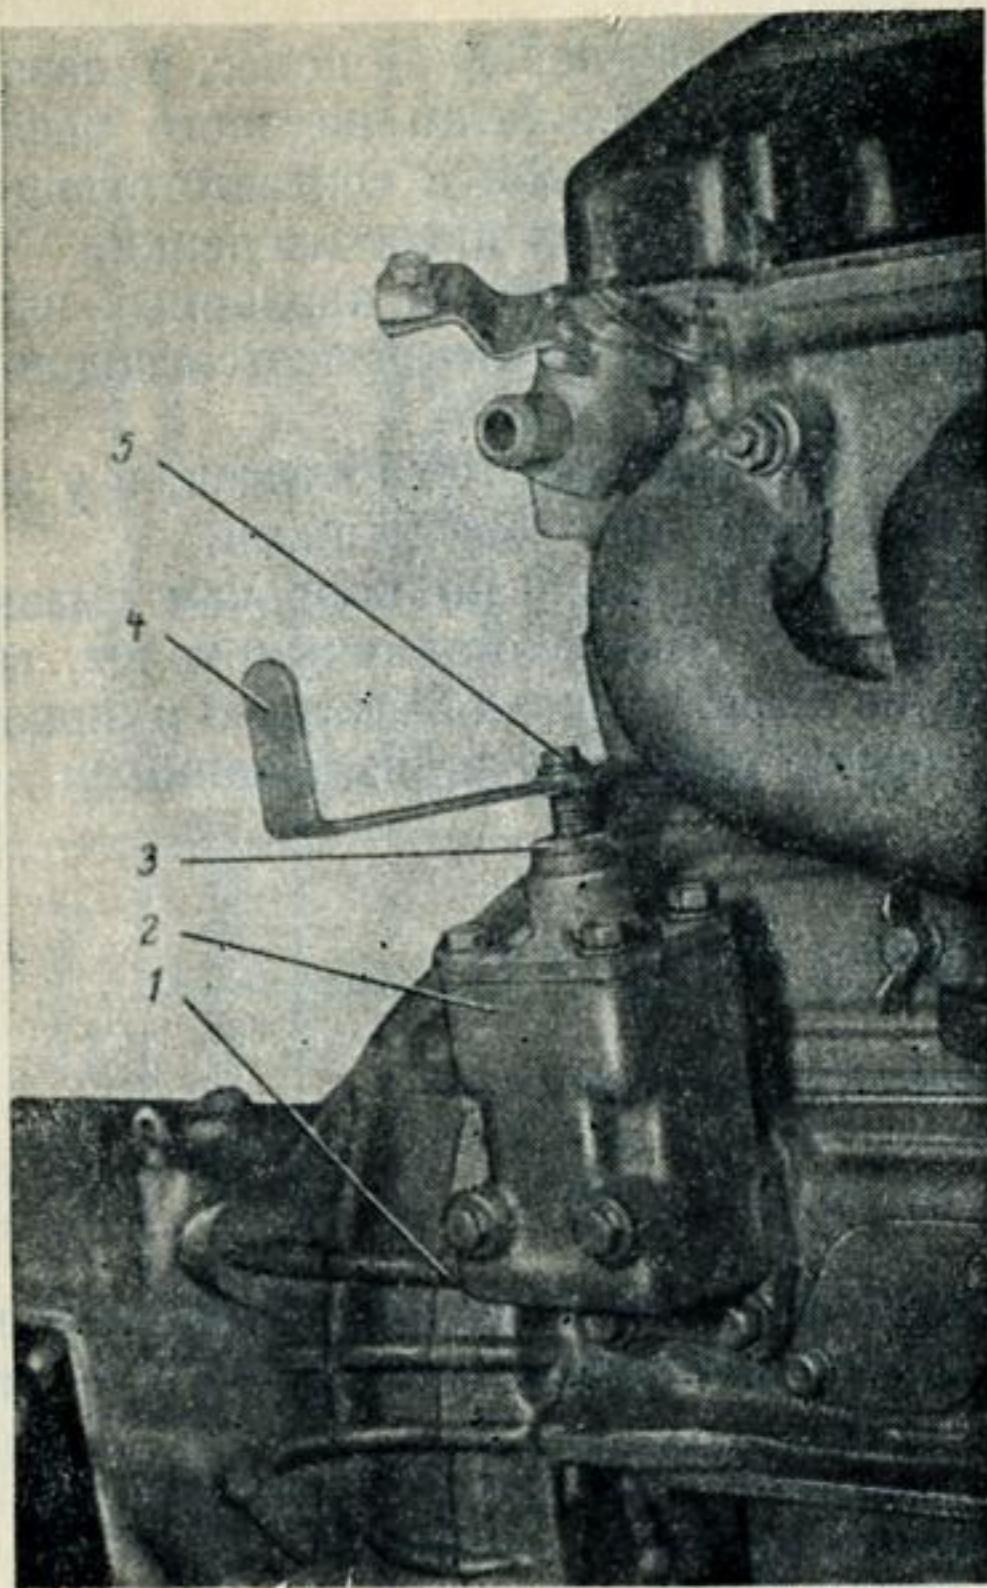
Установка фильтра грубой очистки масла на двигателе:
